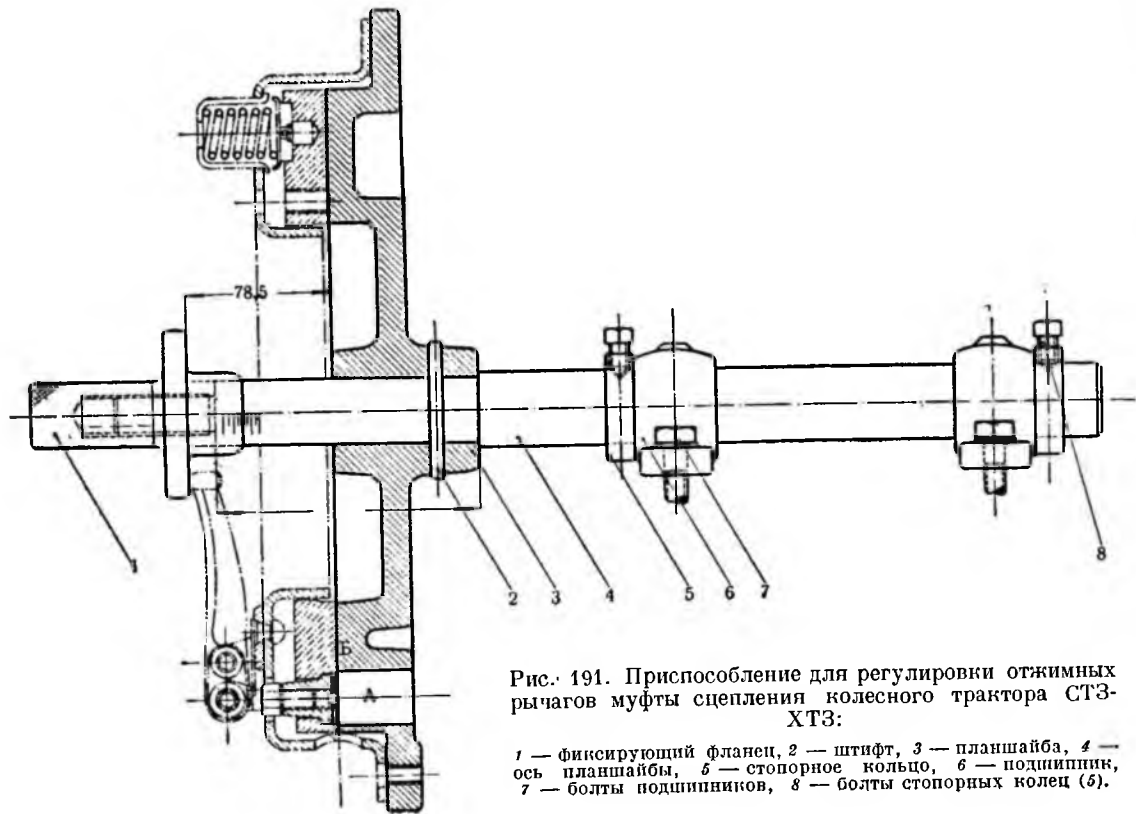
Приспособление для регулировки отжимных рычагов муфты сцепления колесного трактора СТЗ-ХТЗ:
